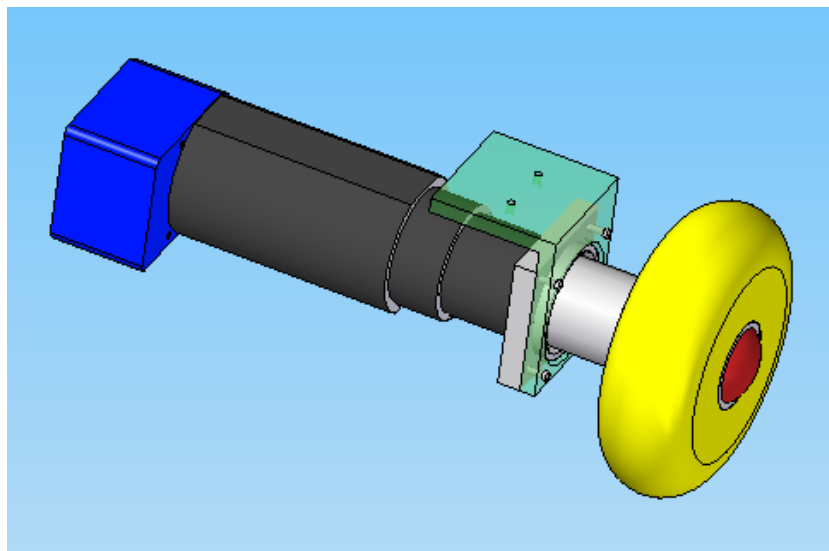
Conjunto motor-rueda diseñado en Solid Edge
